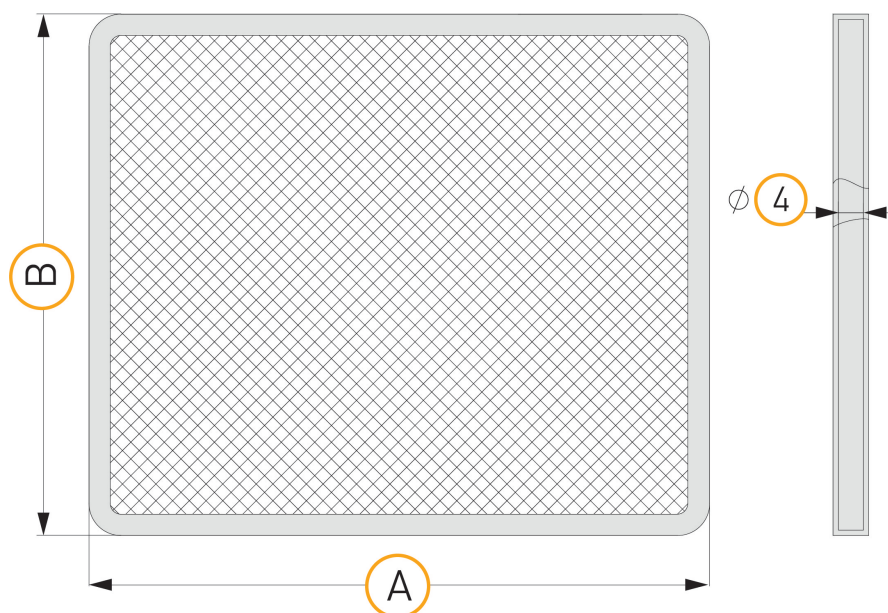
Внешний вид и основные размеры фильтрующих вставок SKF
